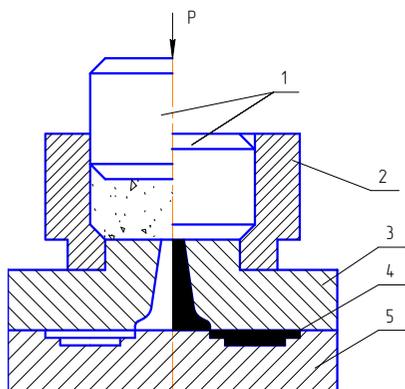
Схема литьевого прессования: 1 – пуансон; 2 – загрузочная камера; 3 – литниковая плита; 4 – изделие; 5 – матрица
